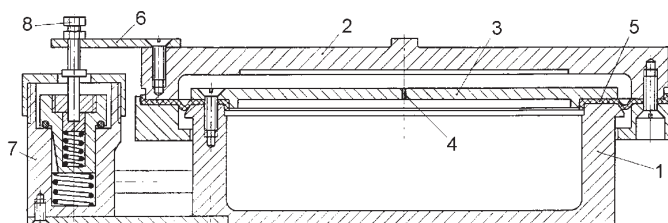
Конструктивная схема пневматической виброизолирующей системы:
